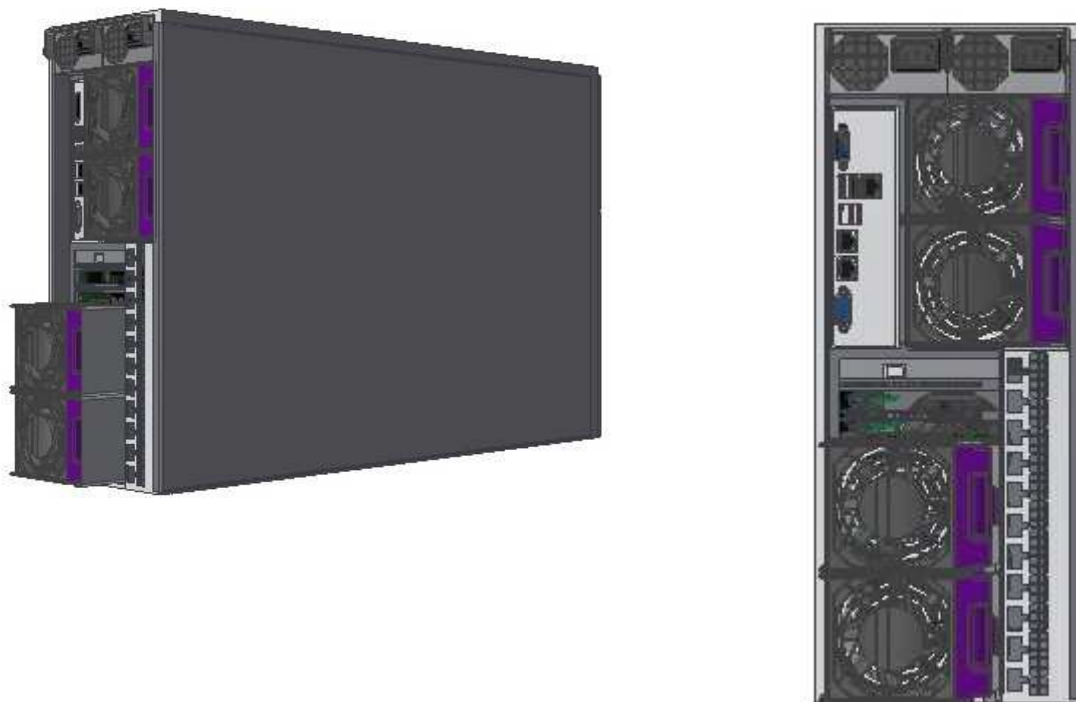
Схема охлаждения корпуса системного блока ПГВС
